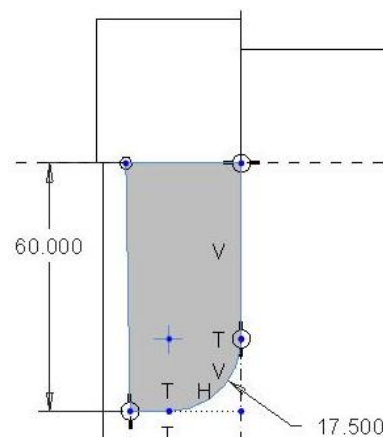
Skizze Anguss Ölablassschraube und Schauglas
